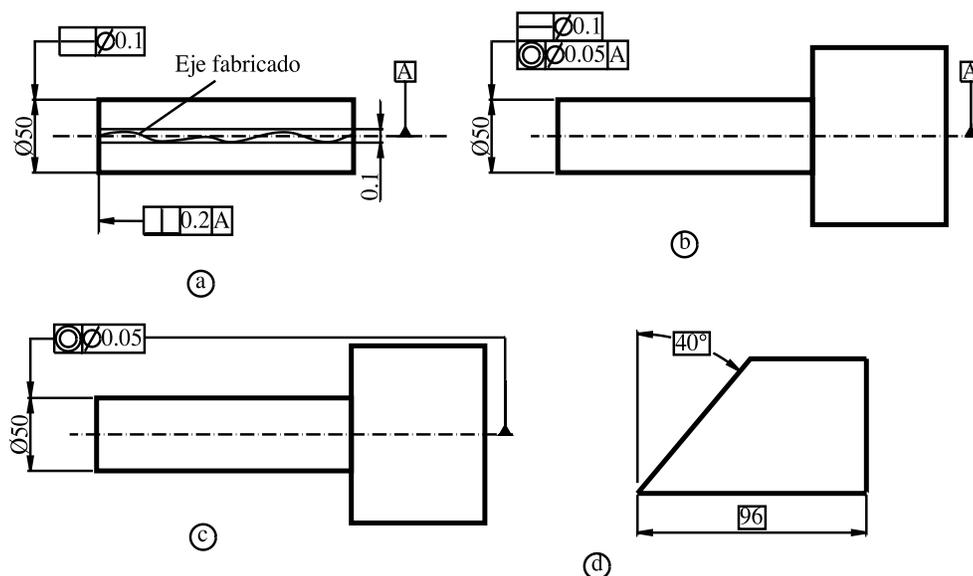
Indicación de las tolerancias geométricas en el dibujo técnico.
